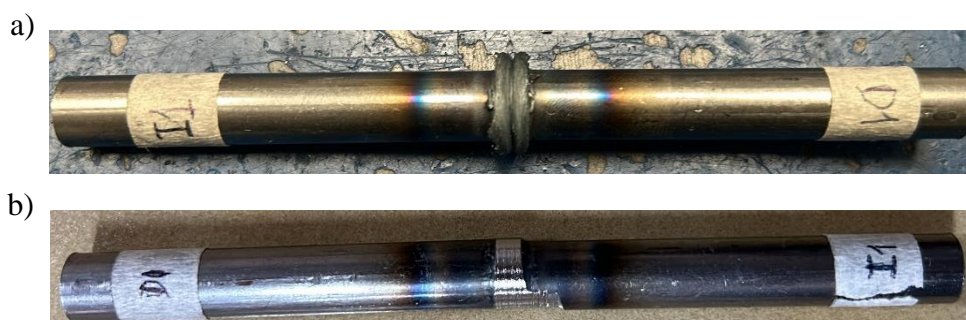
Soldadura a fricción, a) con rebaba, b) mecanizado
